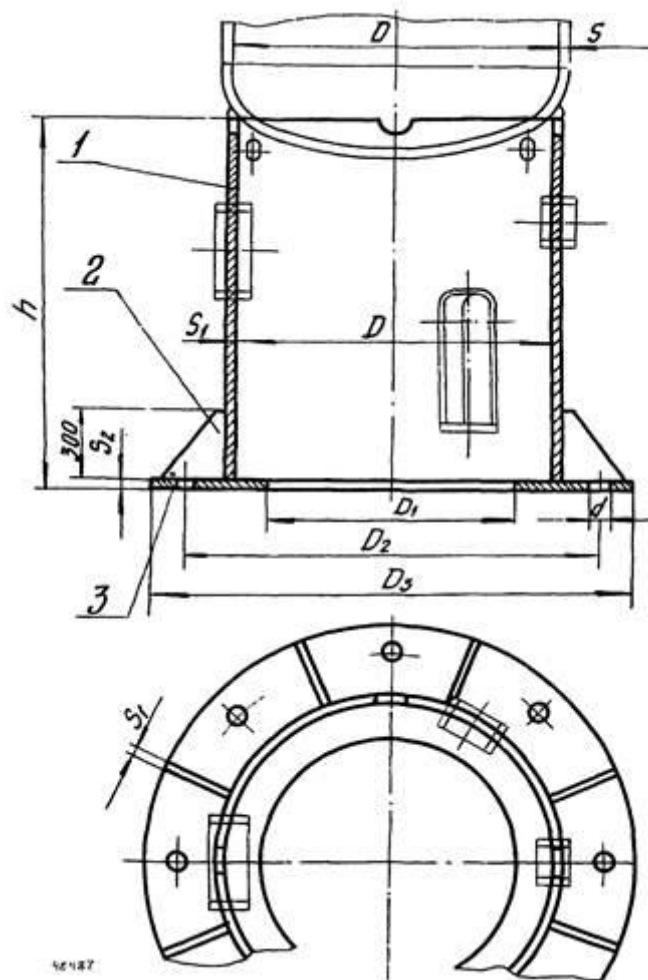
Опора циліндрична з місцевими косинками
